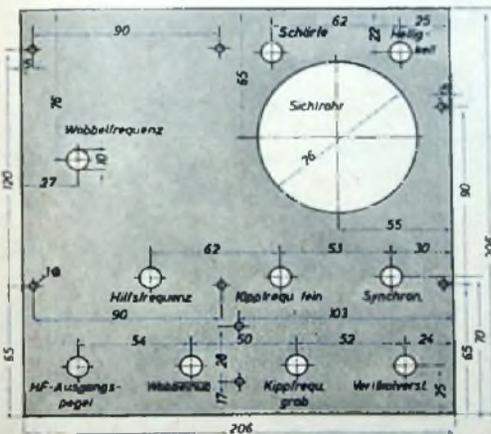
Bohrskizze für die Frontplatte. Material: 2 mm Aluminiumblech
